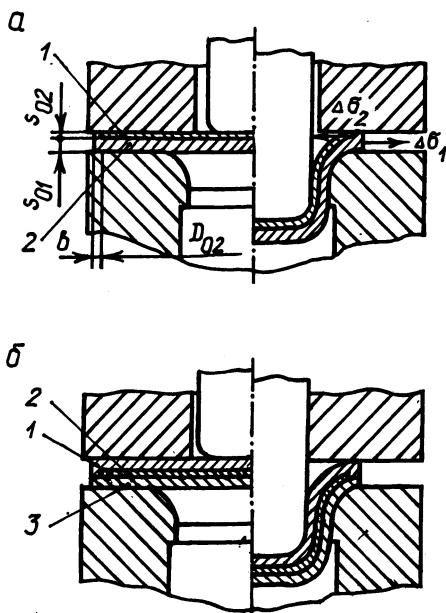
Схема вытяжки двухслойной (а) и трехслойной (б) заготовок с подпором мягкого слоя:
